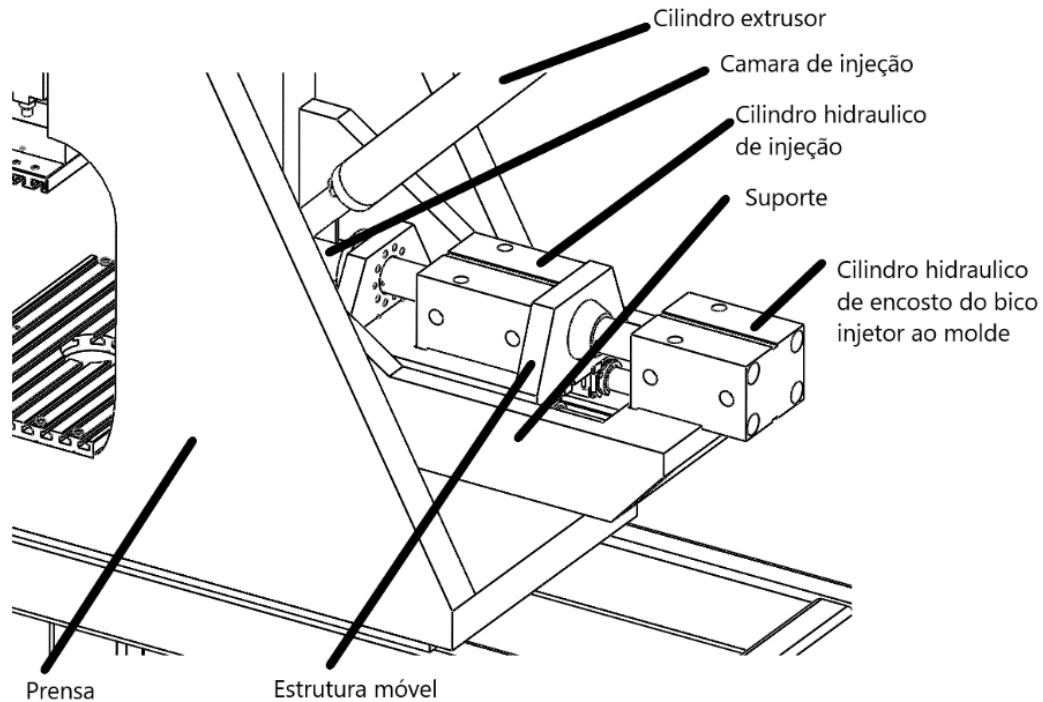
Esboço da estrutura móvel inicial do conjunto constituído pela parte injetora e parte extrusora
